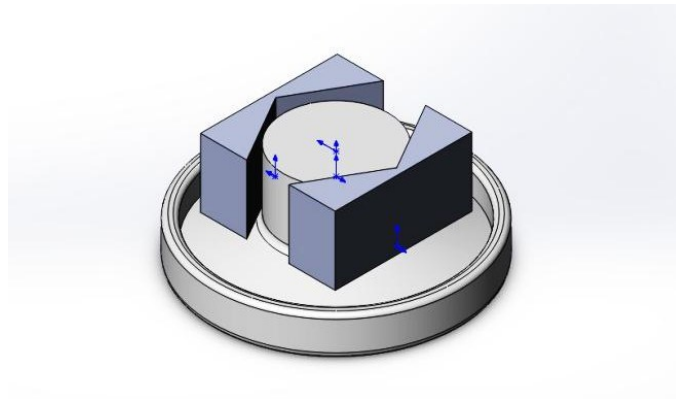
3D – сборка обрабатываемой детали с зажимными элементами
